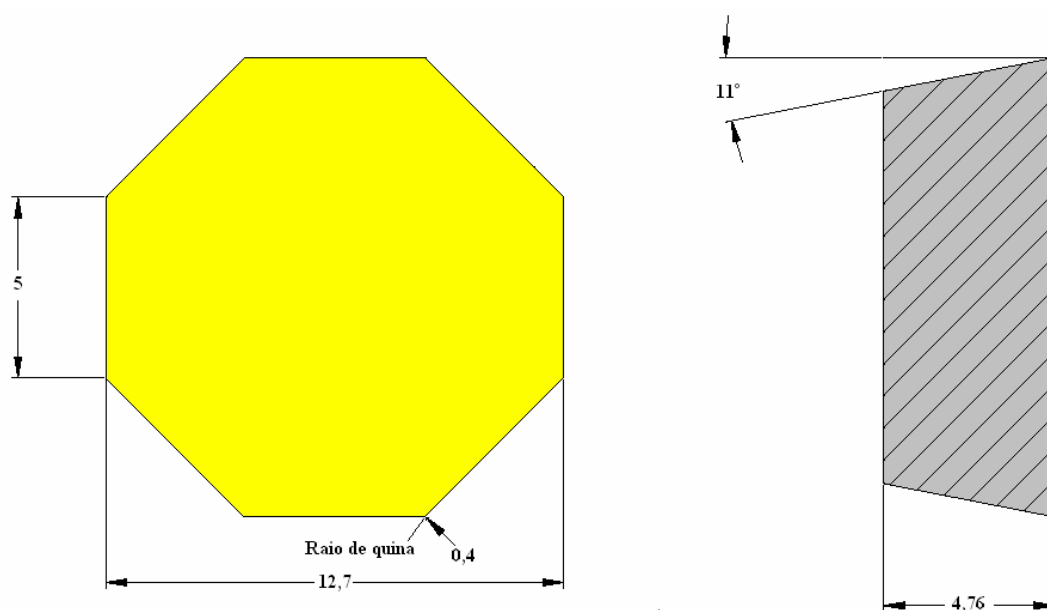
Desenho ilustrativo com as dimensões dos inseros.
